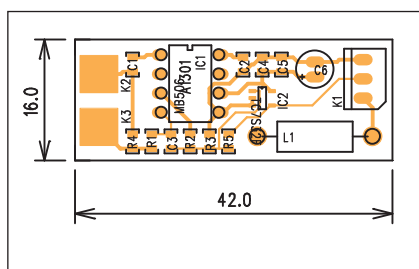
Obrazec desky spojů displeje (strana TOP)
